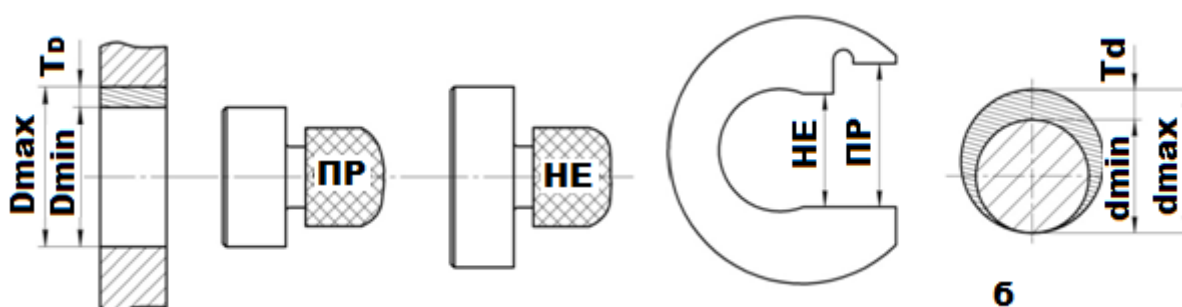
Схемы контроля гладкими предельными калибрами отверстия (а) и вала(б)
